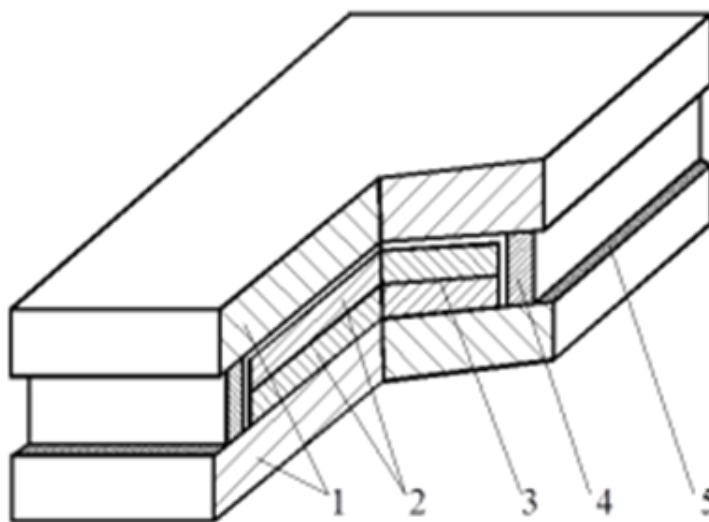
Конструкції пакетів для з'єднання прокатуванням:
